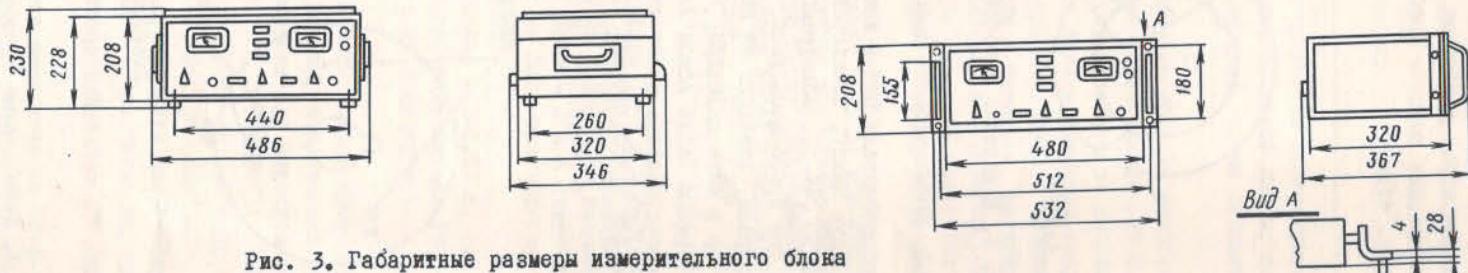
Габаритные размеры измерительного блока вакуумметра ВИТ-3
